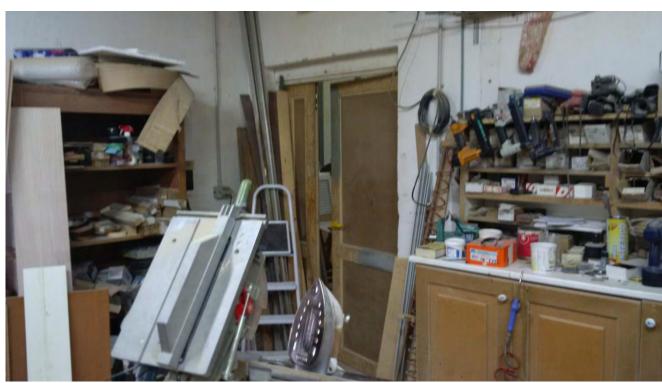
FALEGNAMERIA LOC.1 scatto 03
